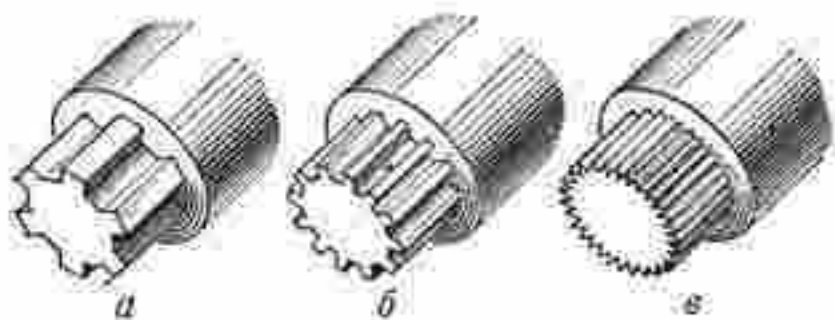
Основные типы зубчатого соединения: а — прямобоочное; б — эвольвентное; в — треугольное.
